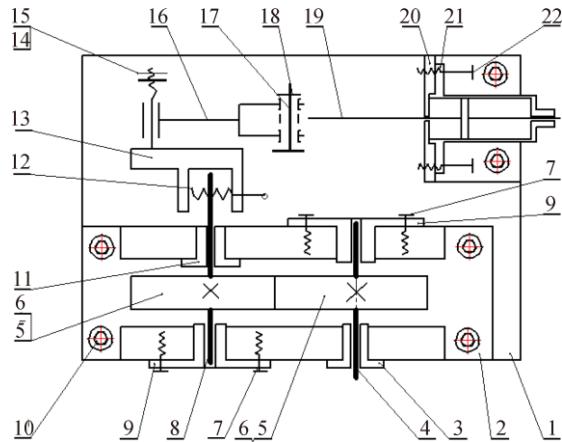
齿轮传动偏心滑块机构装配示意图
